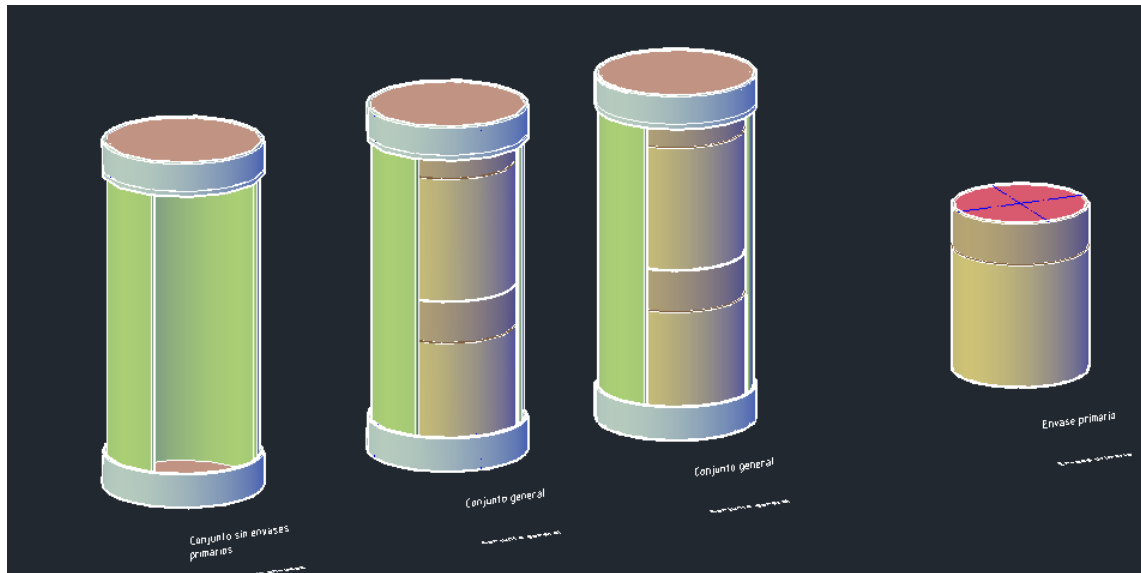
Moldeado 3D 2º Rediseño envase (1)
